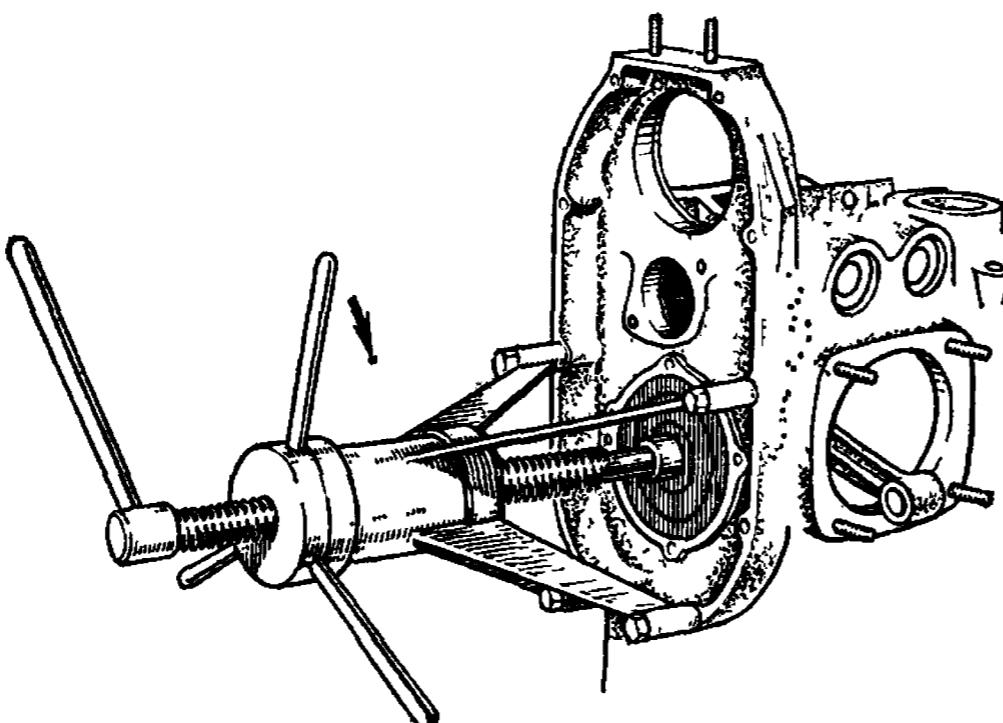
Втягивание конца коленчатого вала в передний подшипник
